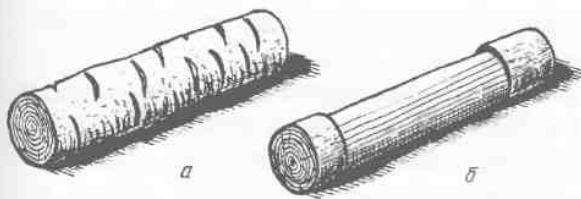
Заготовка кряжа древесины для естественной сушки: а — с поперечными прорезами коры; б — с удалением основной массы коры в серединной части
